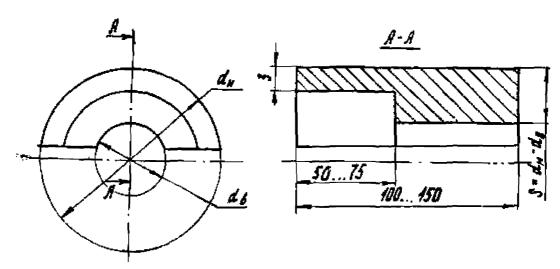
Стандартный образец для настройки упытразвукового прибора при контроле отвода:
